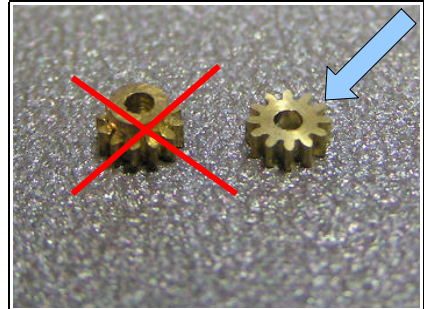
Das Zahnrad mit 12 Zähnen wird als Motorritzel benötigt (Zahnrad ohne Bund)
